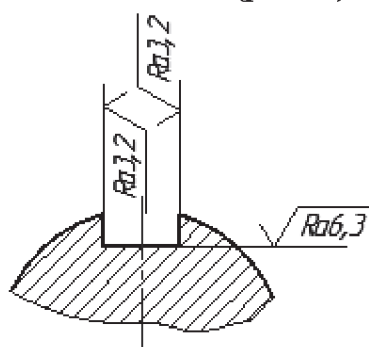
Обозначение шероховатости поверхностей шпоночного паза
